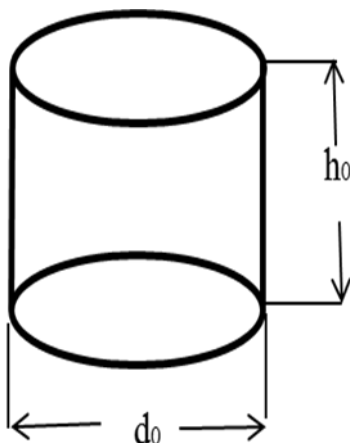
Образец для испытания на сжатие металлов и сплавов
